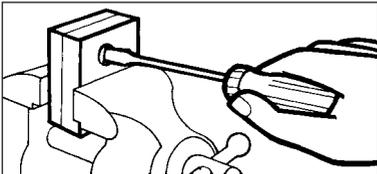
Sicherer Umgang mit Schraubendrehern
